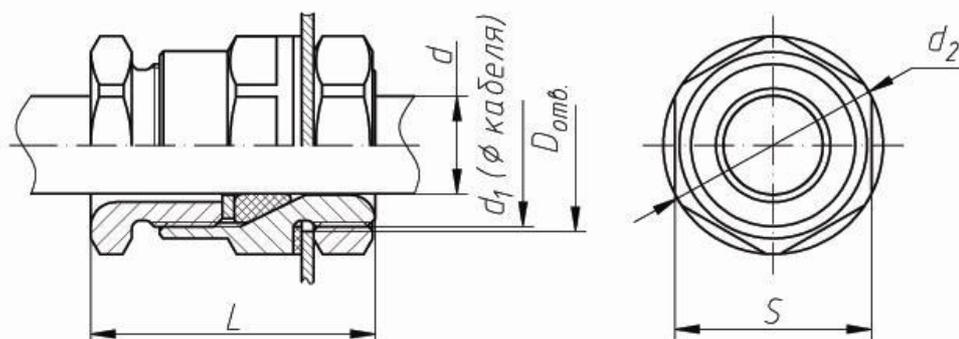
Кабельный ввод для открытой прокладки кабеля (тип
